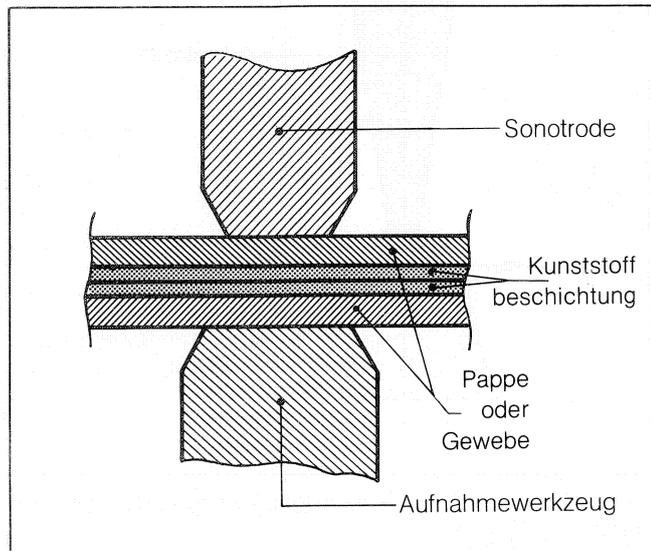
Anordnung beim Ultraschallschweißen beschichteter Pappen oder Gewebe
